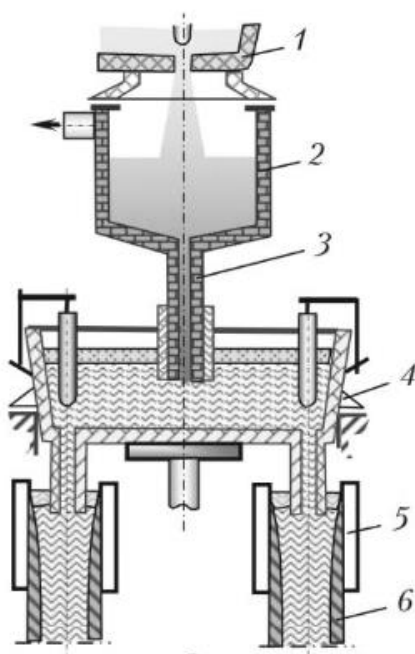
Схема установки поточного вакуумирования при непрерывной разливке стали: 1 – сталеразливочный ковш; 2 – вакуумная камера; 3 – патрубок (металлопровод); 4 – промежуточный ковш; 5– кристаллизатор; 6 - непрерывнолитая заготовка
